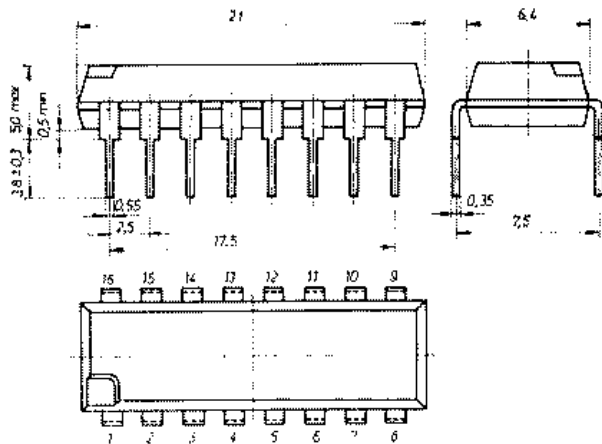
Abmessungen, Bauform K 21.D2.1.16 TGL 26 713
